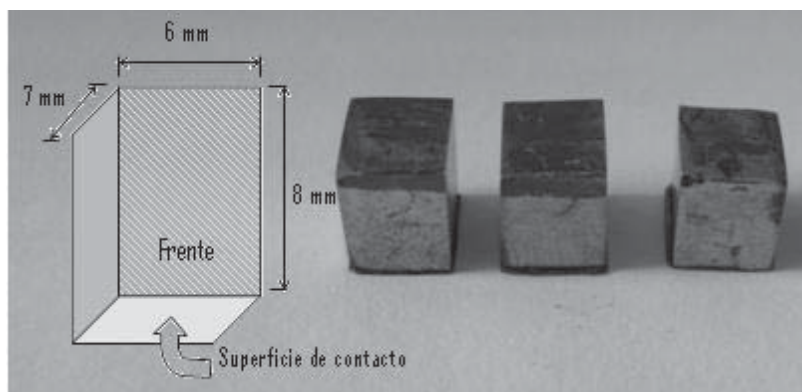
Forma y dimensiones en mm de la probeta a desgastar.
